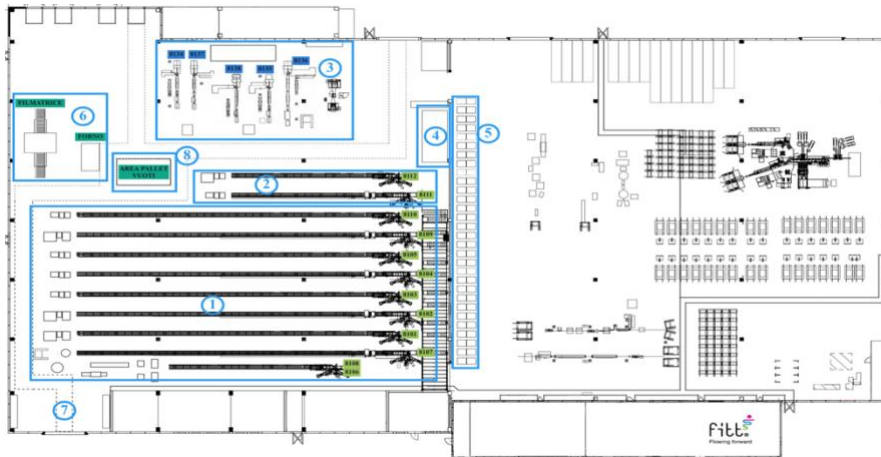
Pianta in scala della terza ipotesi di re-layout (FITT, 2022)
